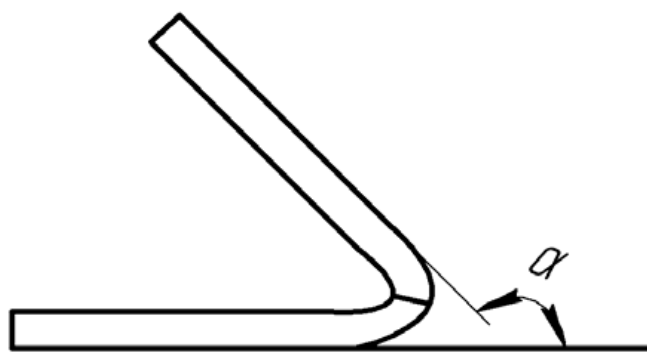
Схема определения угла изгиба сварного соединения
